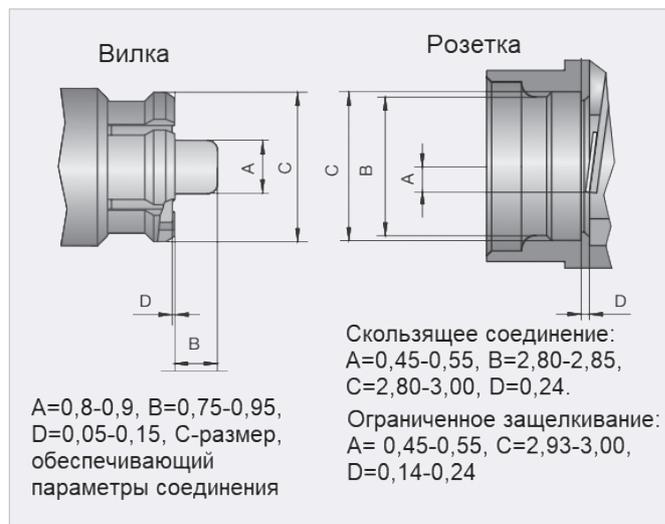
Схема соединения вилки и розетки и размеры, мм, соединителей FMC
